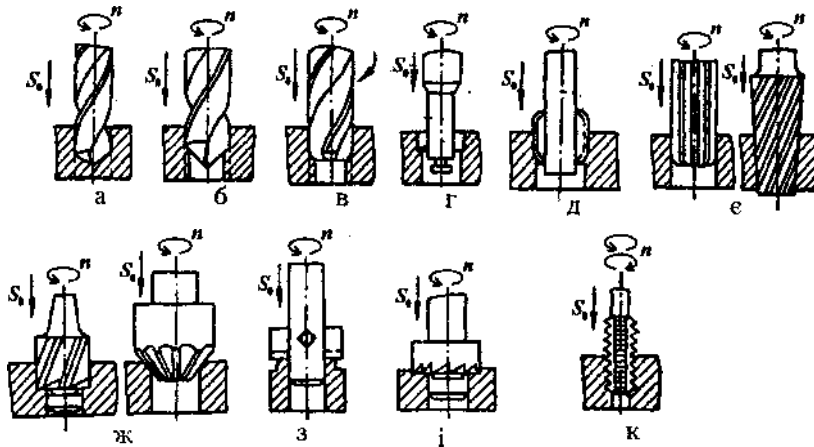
Схеми одержання і обробки отворів на свердлувальних верстатах
